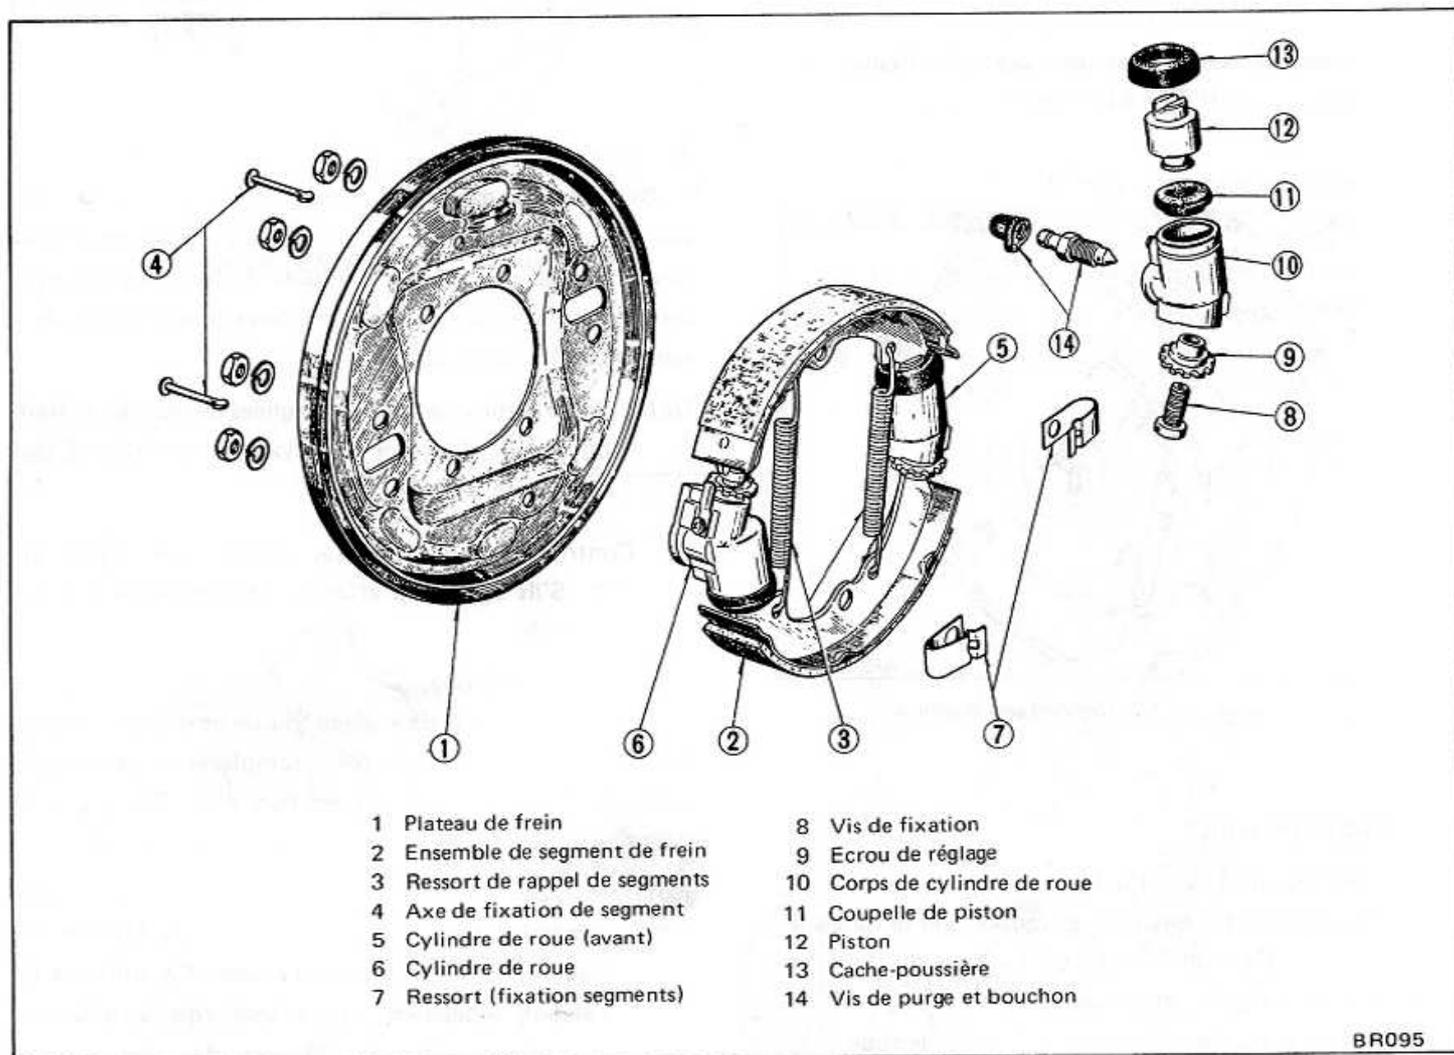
Vue éclatée d'un frein à tambour avant
